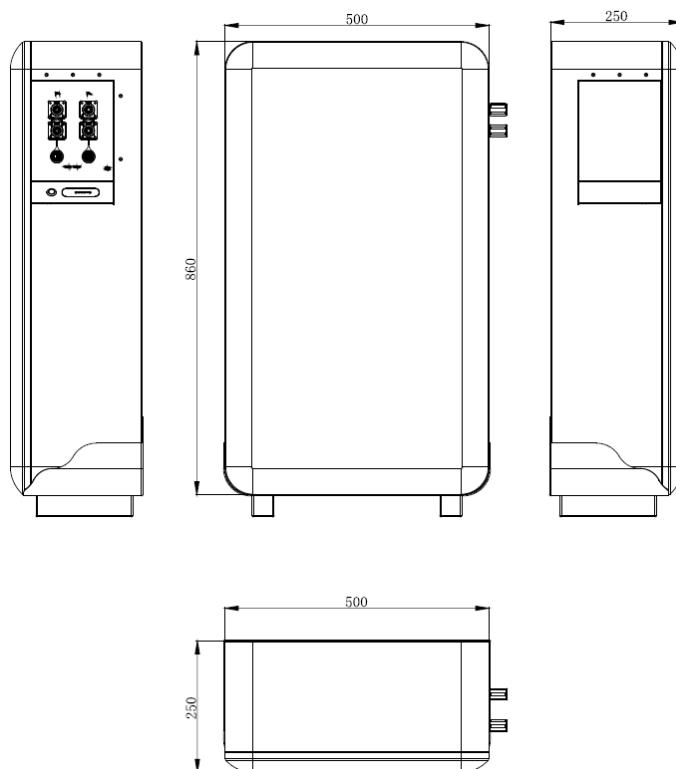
Dimensions du TGP-BAT-LV51-16 (unité : mm)
